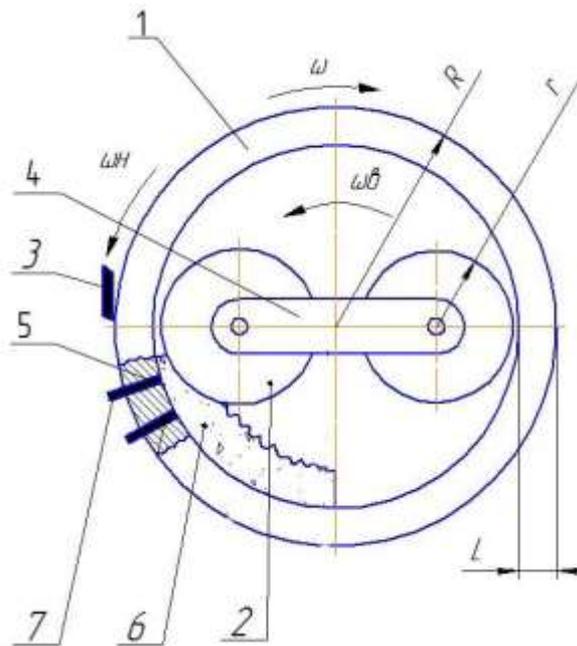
Схема рабочего органа пресс-гранулятора с кольцевой матрицей [7]:
